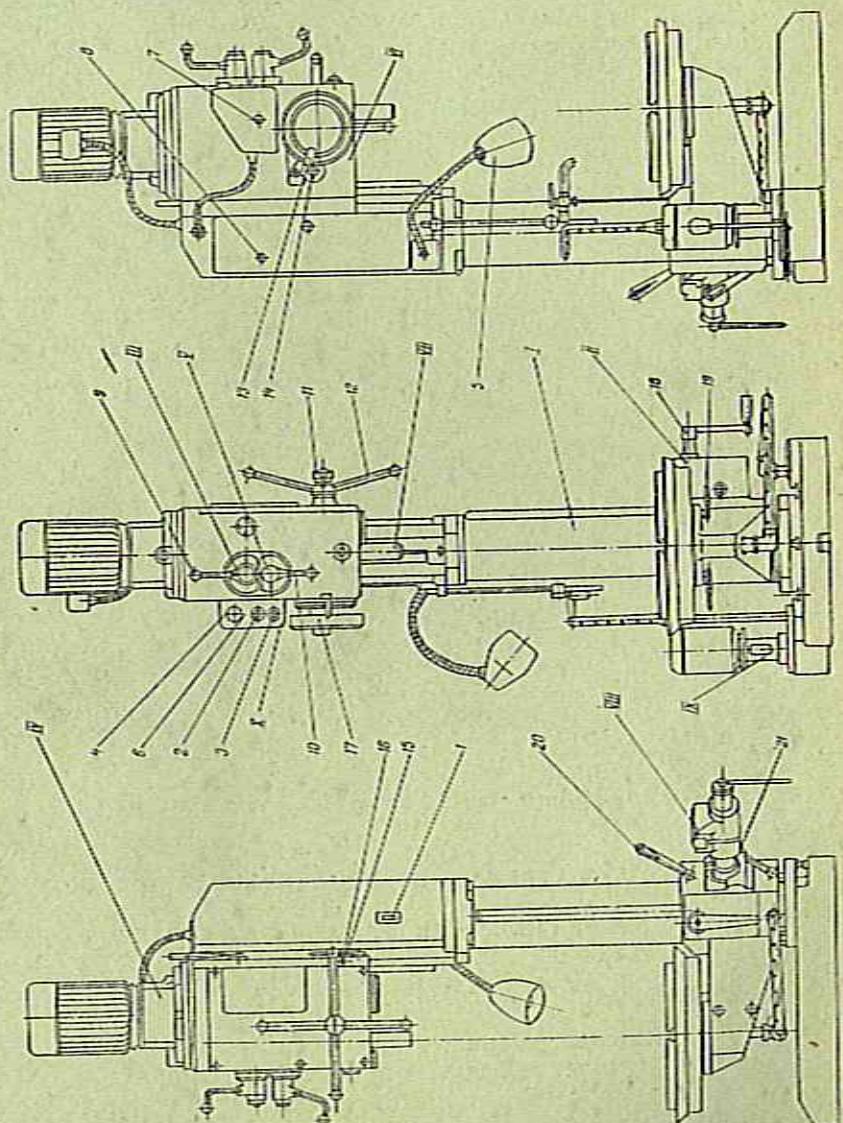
Общий вид станка с обозначением узлов и органов управления.
